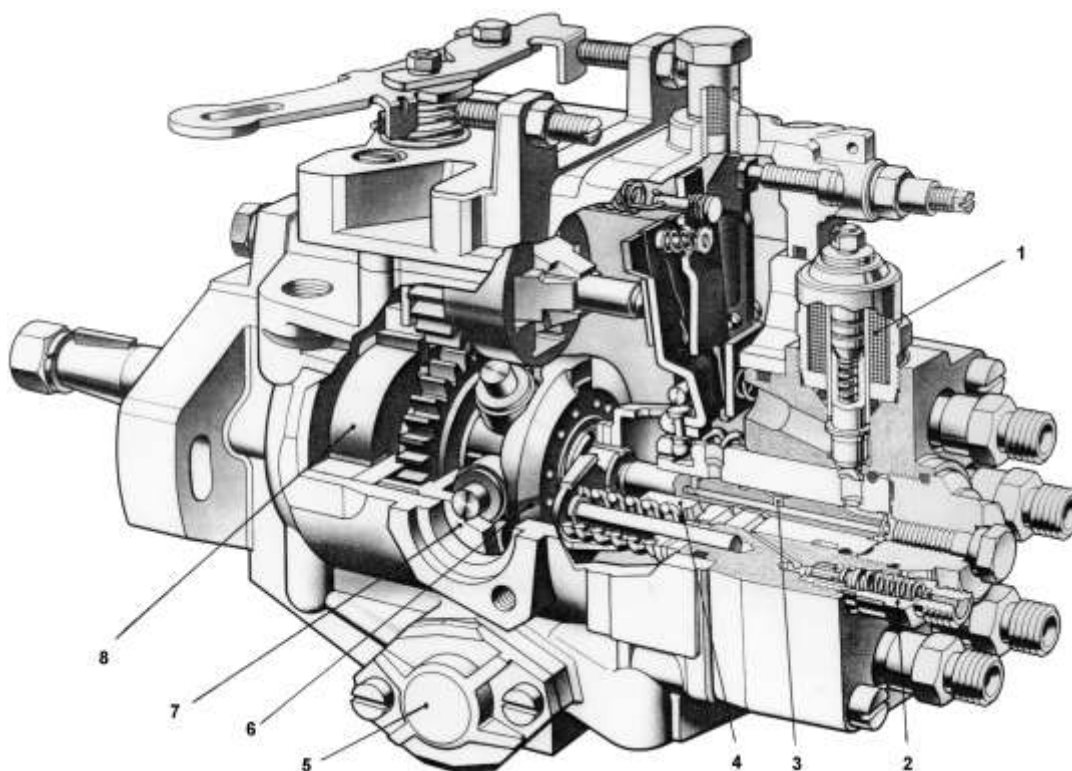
Общий вид ТНВД VE фирмы R.Bosch базовой конструкции с механическим регулятором: 1 - электромагнитный клапан; 2 - штуцер нагнетательного клапана; 3 - выфрезеровка-распределитель; 4 - дозирующая муфта; 5 - автомат регулирования УОВТ; 6 - кулачковая шайба; 7 - обойма с роликами; 8 - ТПН.
